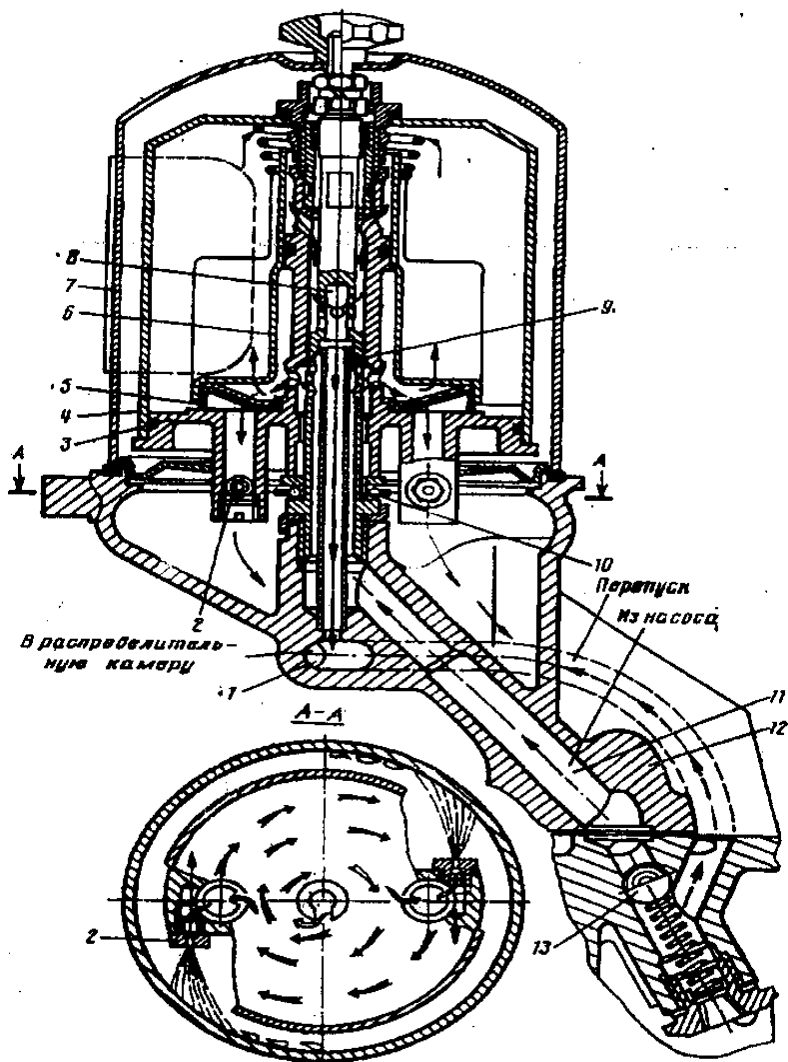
Центробежный фильтр тонкой очистки масла двигателя ЗИЛ – 130
